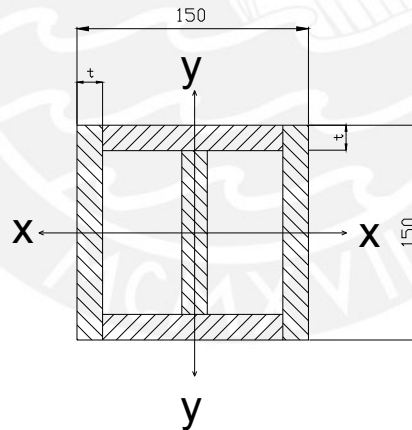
BARRA DE GIRO HORIZONTAL: SECCIÓN A-A
